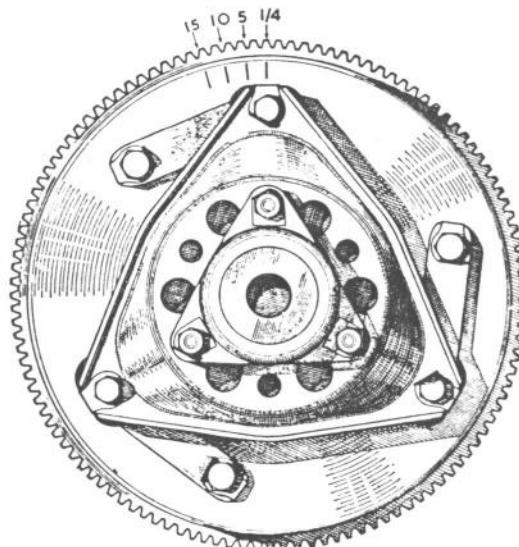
Volante del motor y mecanismo de embrague.
